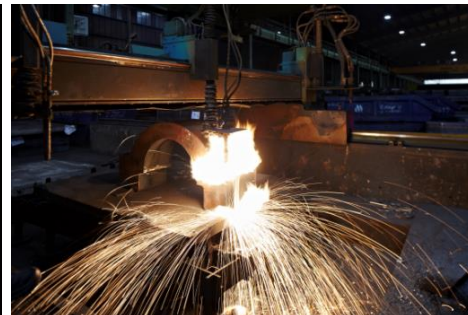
Ein Drittel der 380 von Jebens gefertigten und zu komplexen Baugruppen zusammengefügte Einzelteile wird mechanisch bearbeitet.
